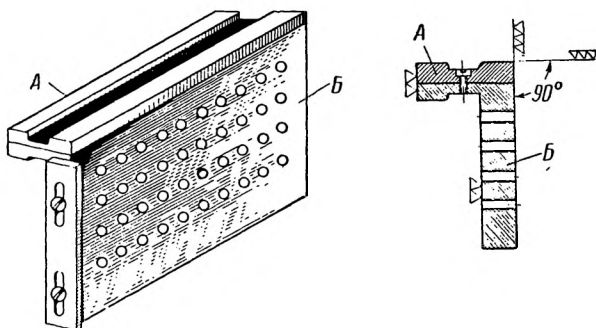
Внешний вид и поперечный разрез наметки универсального типа
